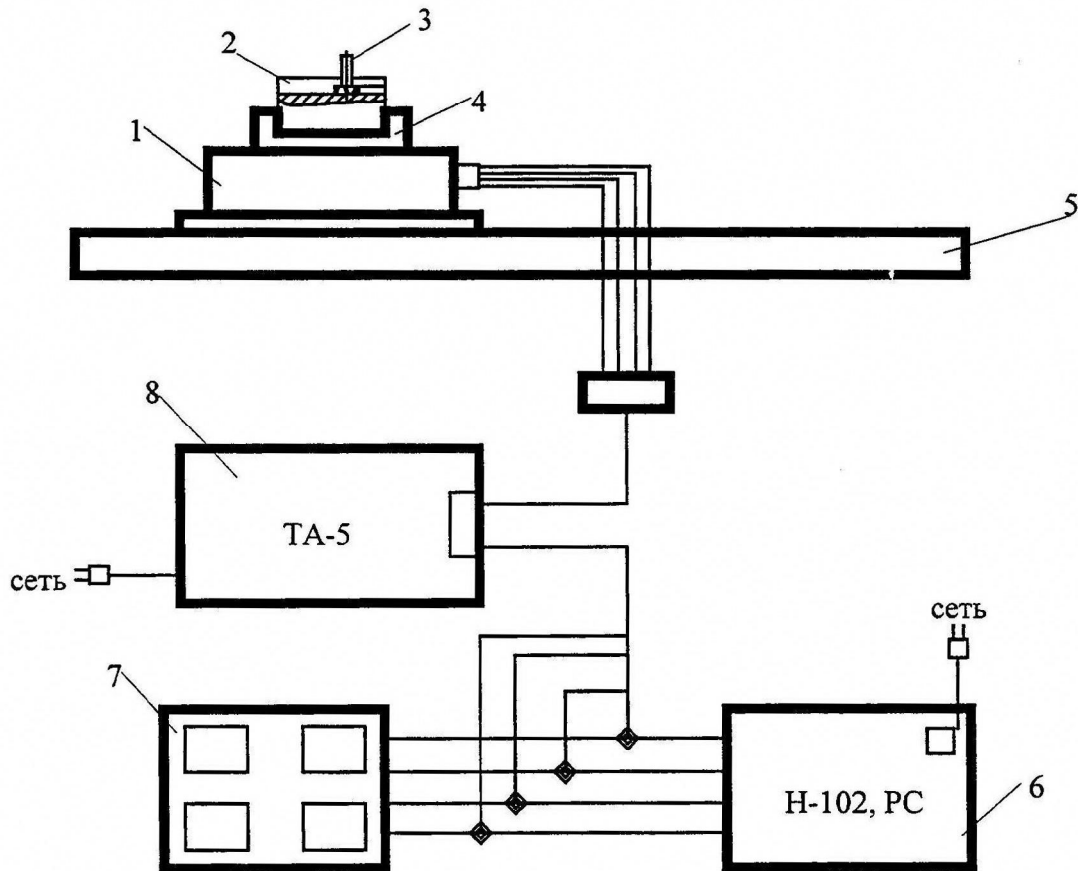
Схема станка для проведения экспериментальных исследований: 1 – динамометр-датчик; 2 – заготовка; 3 – фреза для обработки Т-образных пазов; 4 – столик, используемый при фрезеровании; 5 – стол станка; 6 – прибор фиксирующий показания динамометра-датчика (осциллограф или компьютер); 7 – приборный щит; 8 – тензоусилитель
